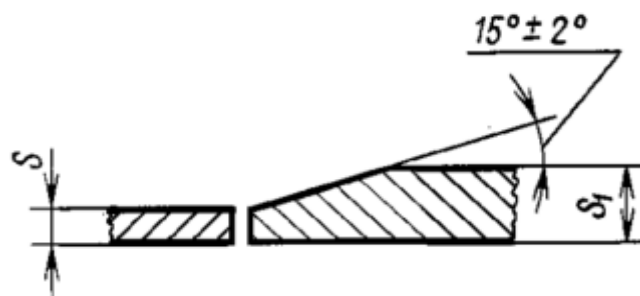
Скос при сварке листов разной толщины
